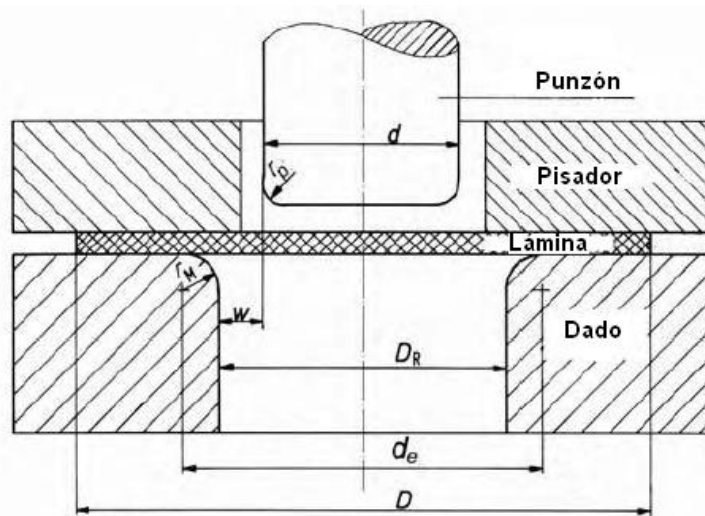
Dimensiones geométricas del punzón, pisador y dado [20].
